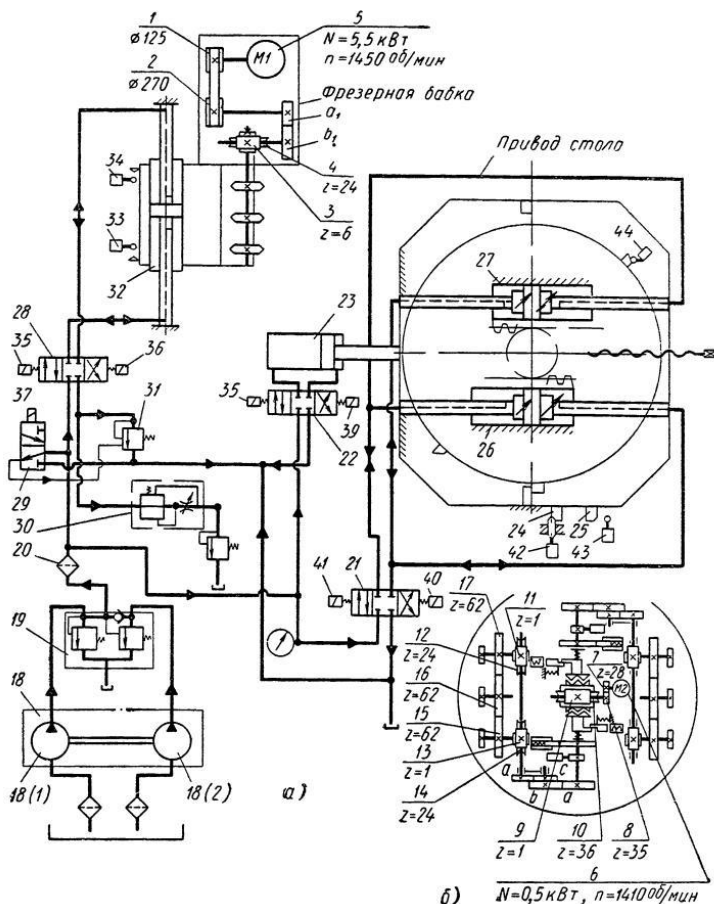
Гидрокинематическая схема зубофрезерного станка ЕЗ-40: а – цепь привода; б – механизм деления; 1, 2 – клиноременная передача; 3, 4 – червячная передача; 5 – электродвигатель привода; 6 – электродвигатель деления; 7-10 – зубчатые колеса; 11-17 – зубчатые передачи; 18 – двойной пластинчатый насос (1-высокого, 2-низкого давления); 19 – разделительная панель; 20 – фильтр пластинчатый; 21 – распределитель поворота стола; 22, 28, 29 – распределитель реверсивный; 23 – гидроцилиндр привода перемещения стола; 24, 25 – упоры; 26, 27 – гидроцилиндры привода поворота стола; 30 – регулятор расхода; 31 – напорный золотник; 32 – гидроцилиндр суппорта; 35-41 – электромагниты; 33, 34, 42, 44 – конечный выключатель
